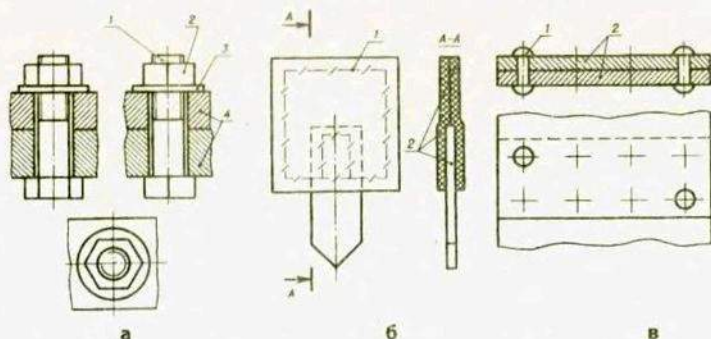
Зображення з'єднань деталей на кресленнях: а — різьбове (1 — болт; 2 — гайка; 3 — шайба; 4 — з'єднувальні деталі); б — ниткове (1 — шов, 2 — з'єднувальні деталі); в — заклепкове (1 — заклепка, 2 — з'єднувальні деталі)
